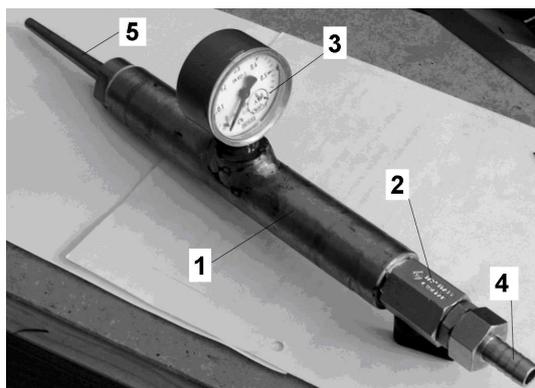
Устройство для пневматического испытания сварного шва на плотность: 1 – ресивер; 2 – запорный кран; 3 – манометр; 4 – входной ниппель; 5 – ниппель присоединительный
